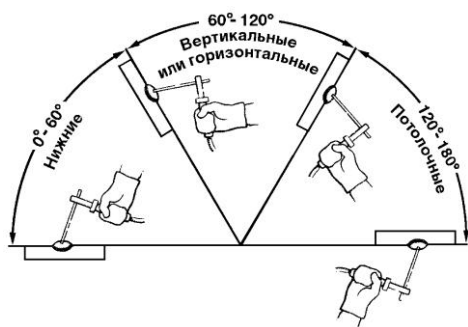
Основные положения сварки и их обозначения
